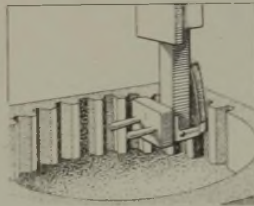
Halb fertige Zahnradform und Ausstechmesser.
